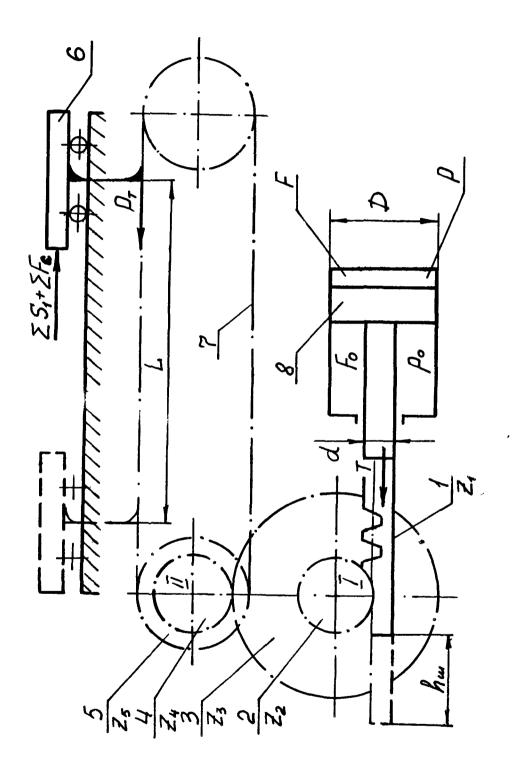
Кинематическая стема метанизма подачи заготовки кареткой с приводом от гидроускорителя (станок ШОІ6-4)
